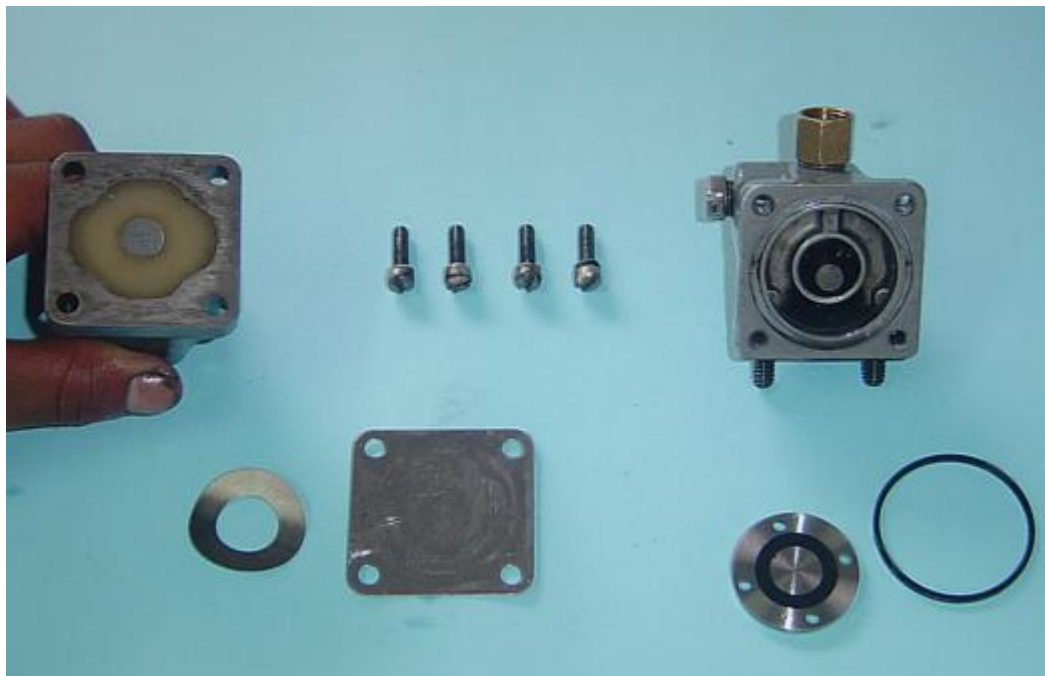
Inspección de la Placa tipo Válvula
